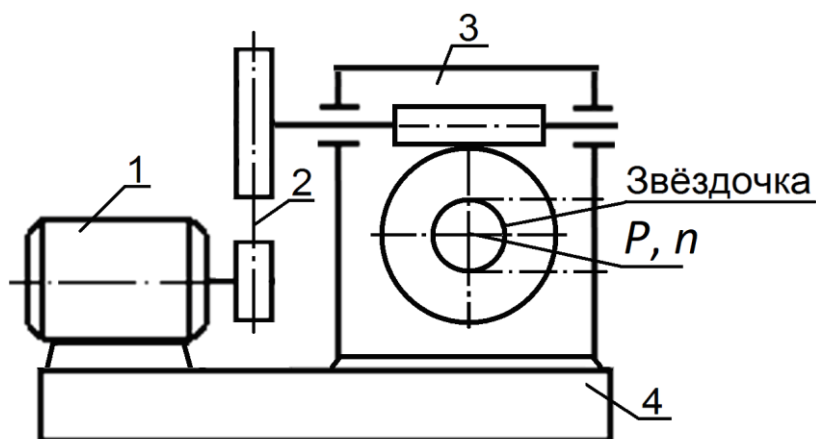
Привод элеватора: 1 – электродвигатель; 2 – вертикальная клиноременная передача; 3 – одноступенчатый червячный редуктор с верхним червяком;
